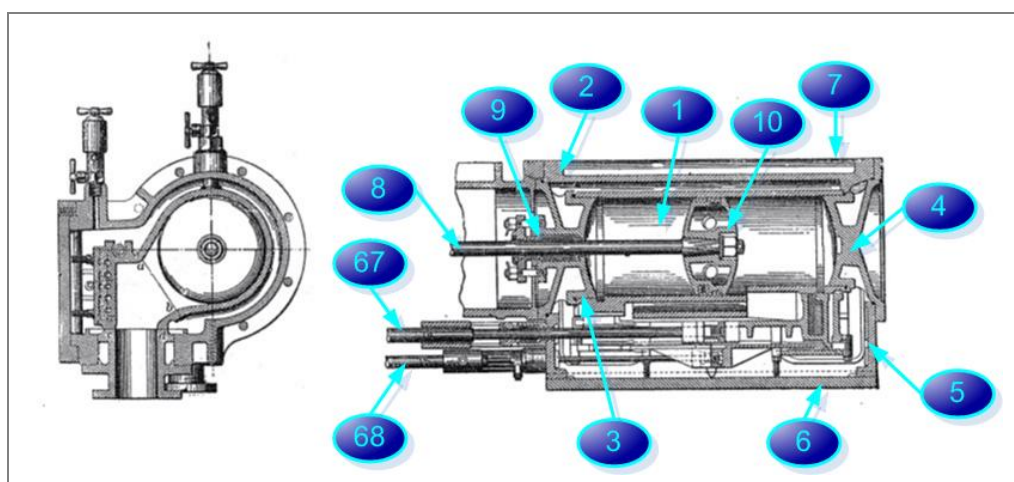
1900 – MACHINE A VAPEUR FIGUET - PLAN DE DETAILS DU CYLINDRE ET DU DOUBLE TIROIR
